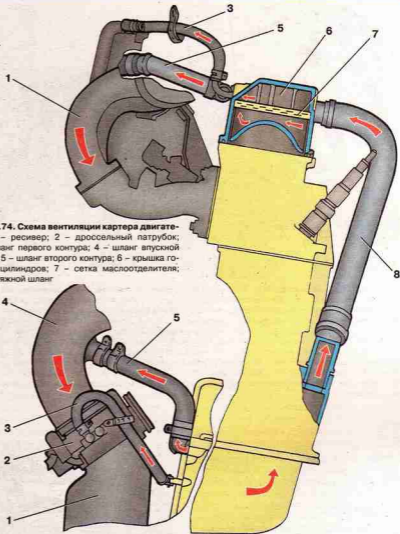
Схема вентиляции картера двигателя: 1 — ресивер; 2 — дроссельный патрубков; 3 — шланг первого контура; 4 — шланг впускной трубы; 5 — шланг второго контура; 6 — крышка головки цилиндров; 7 — сетка маслоотделителя; 8 — вытяжной шланг
